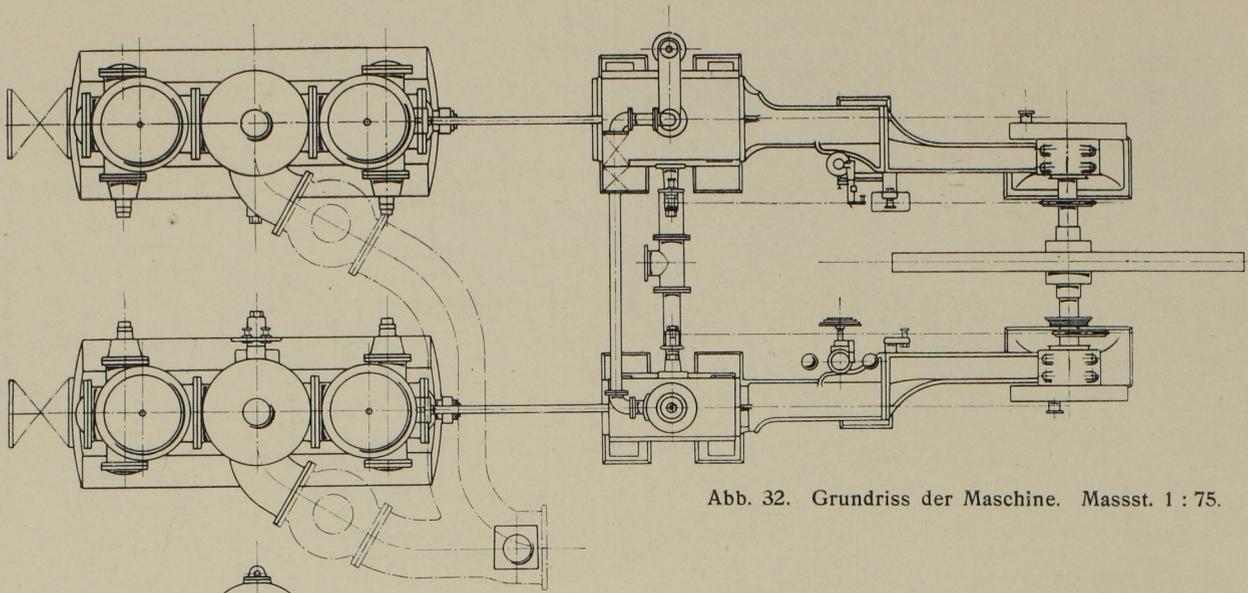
Grundriss der Maschine. Masst. 1 : 75.
